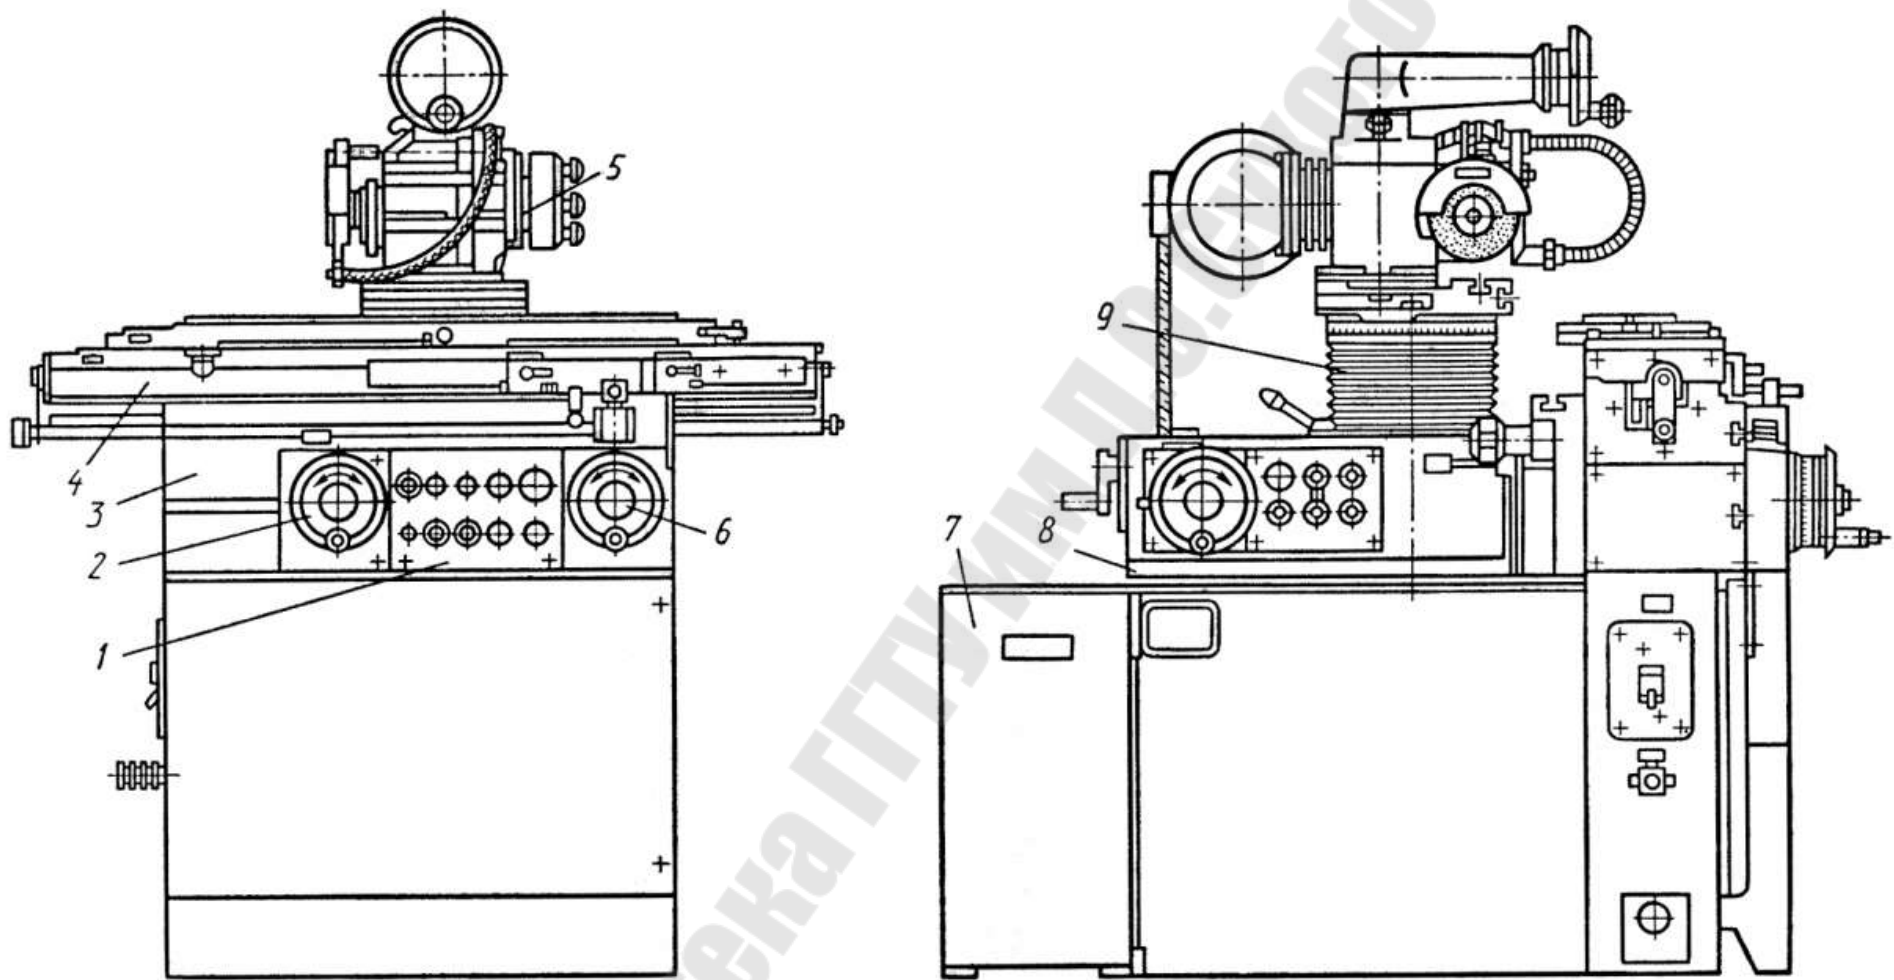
Общий вид универсально-заточного станка 3М642:
